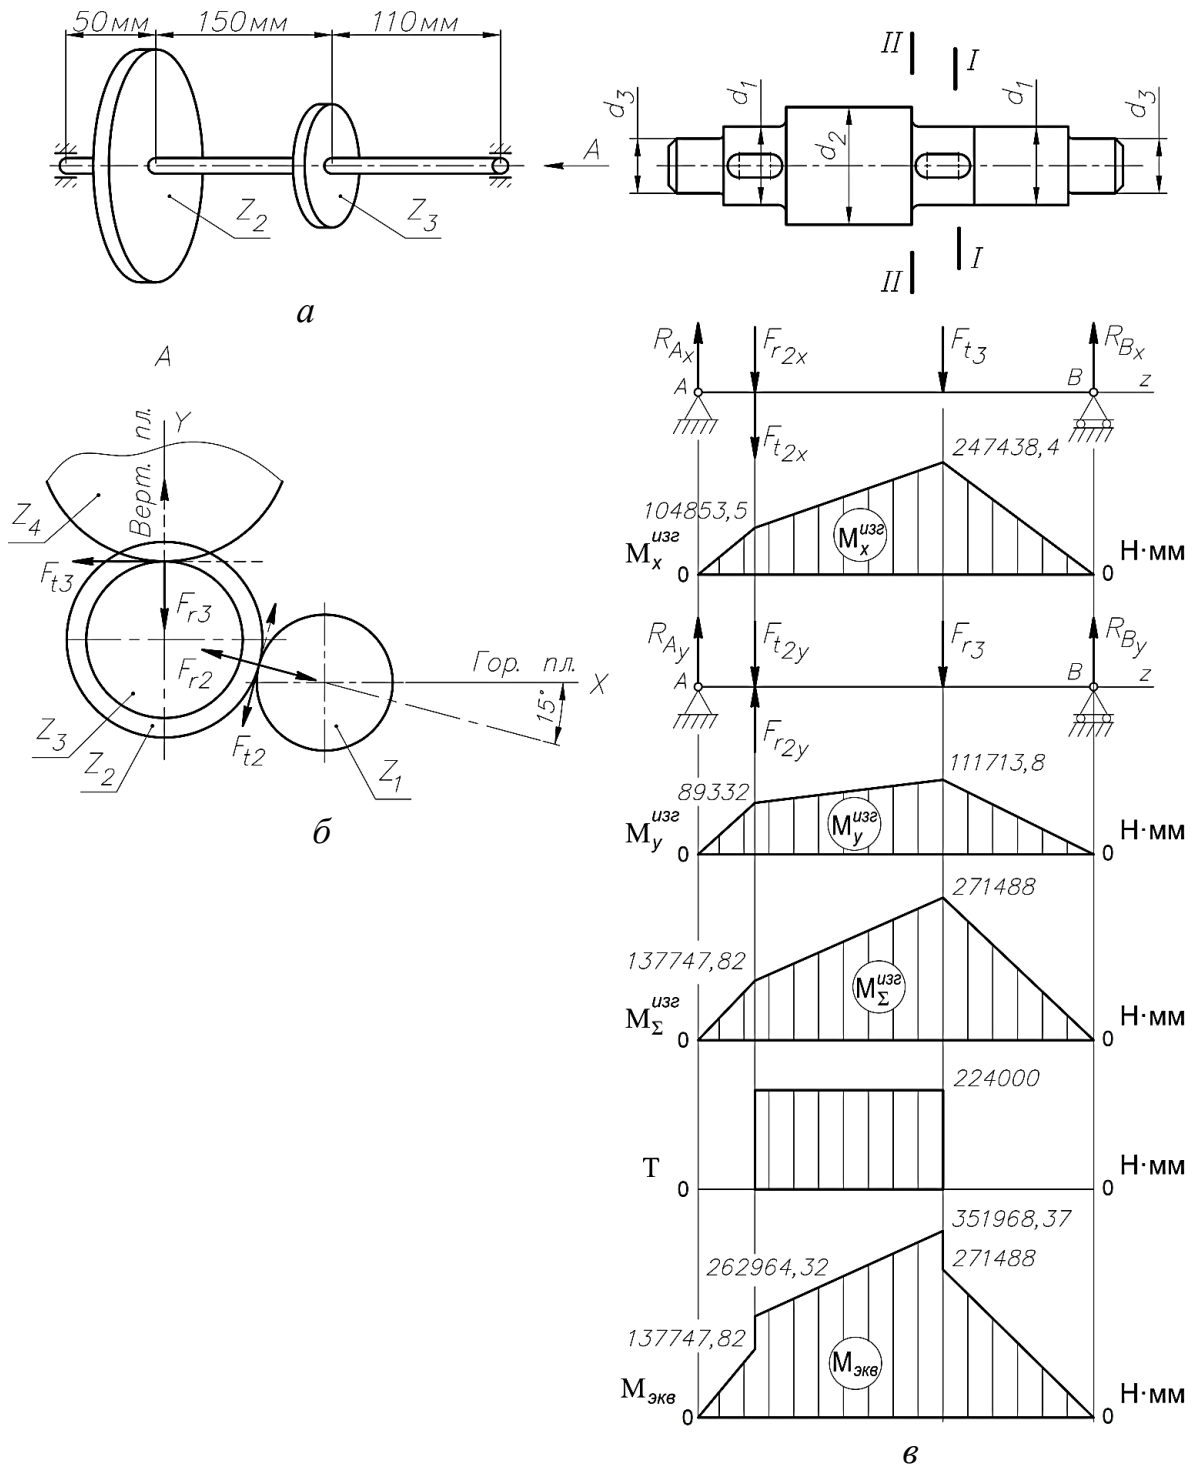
Схема нагрузок и эпюры моментов вала коробки передач
